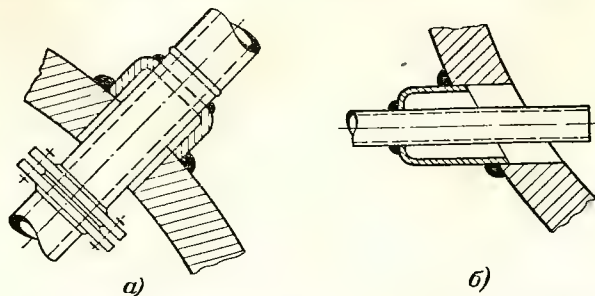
Установка защитных рубашек в местах прохода труб через стенку барабана котла. а—на входе в котел питательной воды; б—на нижнем штуцере водоуказательной колонки.
